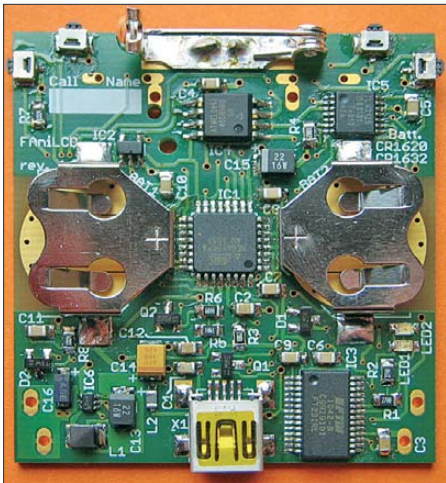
Auf der mit SMD-Bauteilen bestückten Seite ist auch die Broschnennadel aufzulöten.
